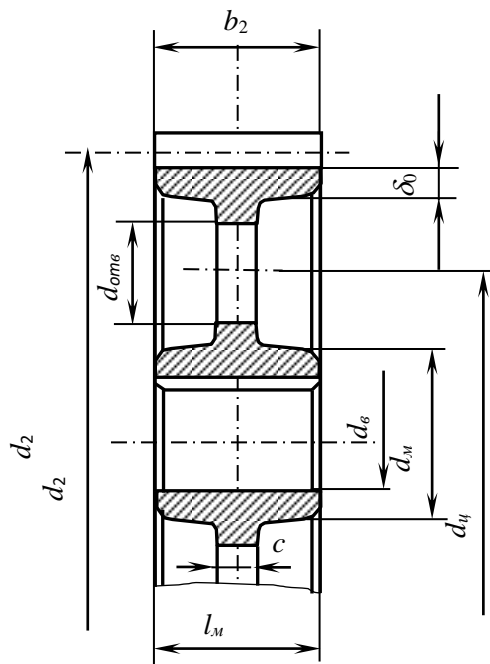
Конструювання циліндричних зубчастих коліс
